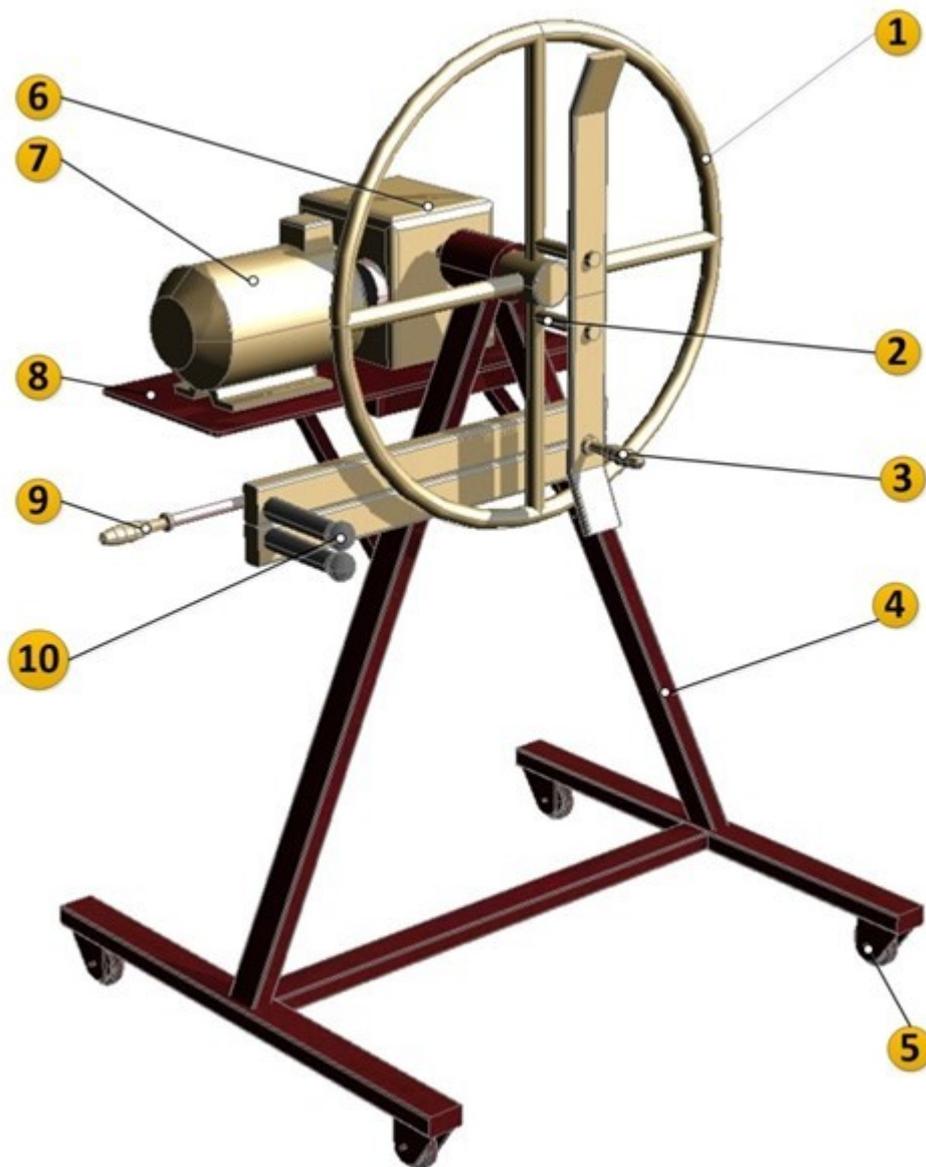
Устройство для скатки и перекатки пожарных напорных рукавов: 1 — колесо со спицами; 2 — штырь со съемной втулкой и прижимом; 3 — рукоятка; 4 — рама сварная; 5 — колесо (ролик); 6 — редуктор червячный; 7 — электродвигатель; 8 — кронштейн; 9 — рычаг подвижный; 10 — ригели направляющие.
